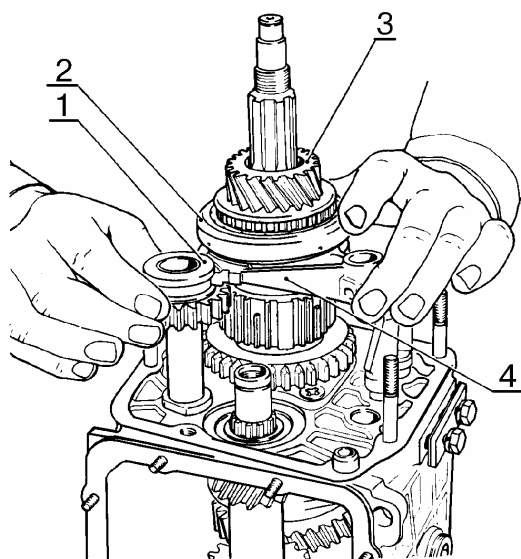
Снятие промежуточной шестерни заднего хода, шестерни V передачи в сборе с синхронизатором и вилкой:
